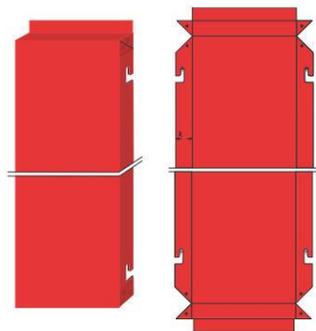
Распространенный вид кассеты и раскрой заготовки
